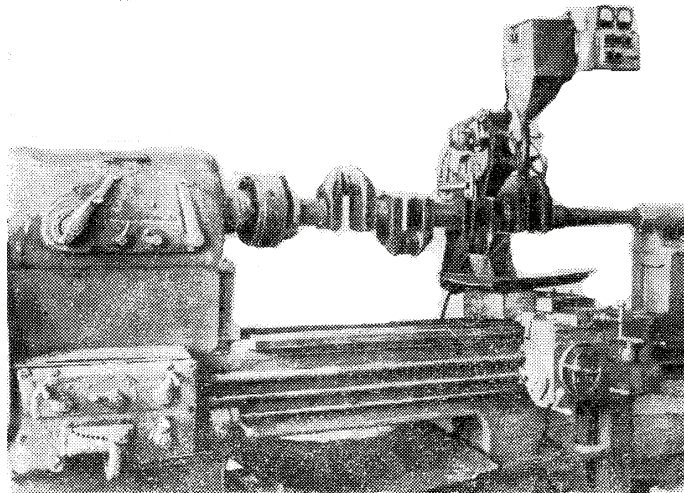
Токарний верстат, пристосований для наплавлення колінчатих валів під шаром флюсу
